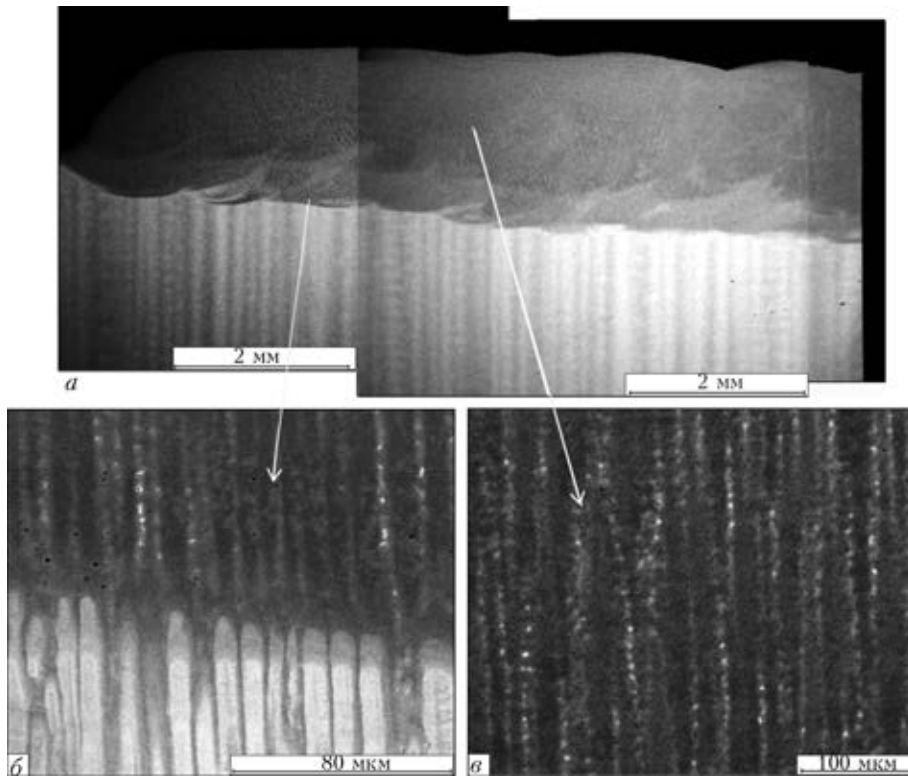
Микроструктура продольного сечения шва, наплавленного по торцу монокристалльной лопатки с использованием присадочного сплава IN625: *a* — общий вид шва; *б* — линия сплавления; *в* — наплавленный металл
